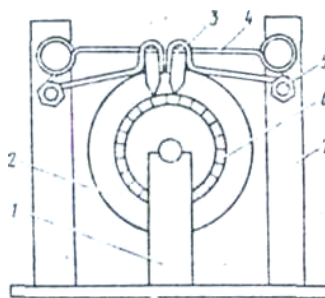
Прилад для вимірювання омичного опору обмотки якоря
